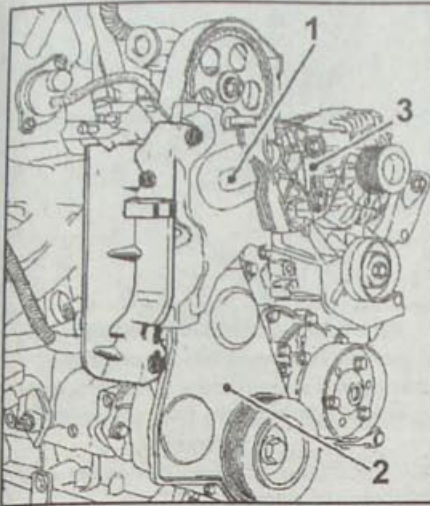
Расположение верхнего (1) и нижнего (2) кожухов ремня привода газораспределительного механизма и кронштейна маятниковой подвески (3)
